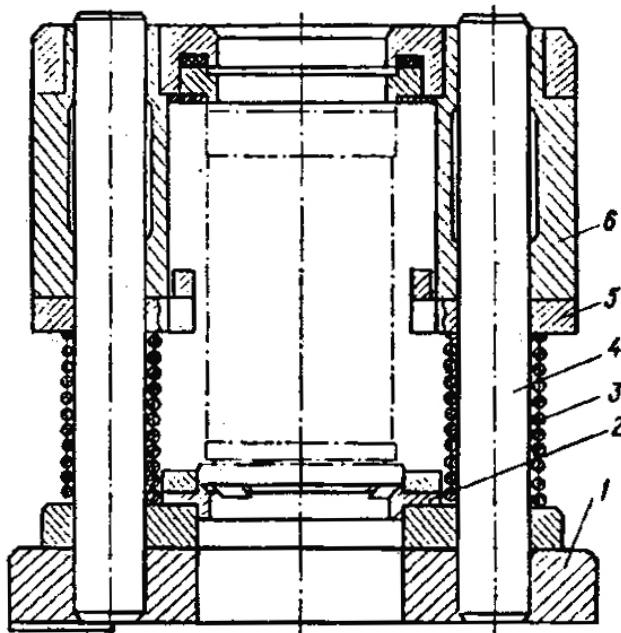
Затискний пристрій для встановлення гільзи циліндра під час розточування: 1 – станина; 2 – упорне кільце; 3 – пружина; 4 – напрямна колонка; 5 – шип; 6 – напрямна втулка
